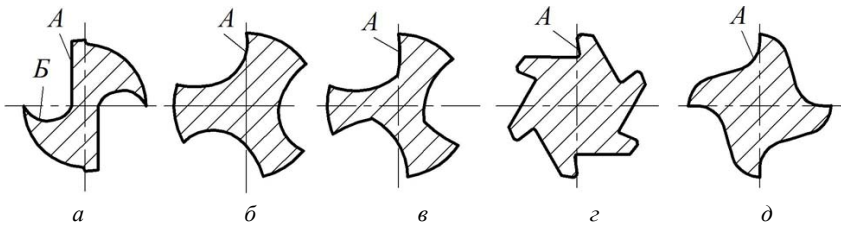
Форма стружечных канавок спирального сверла (а), метчика (б), зенкера (в), развертки (г), фрезы (д)
